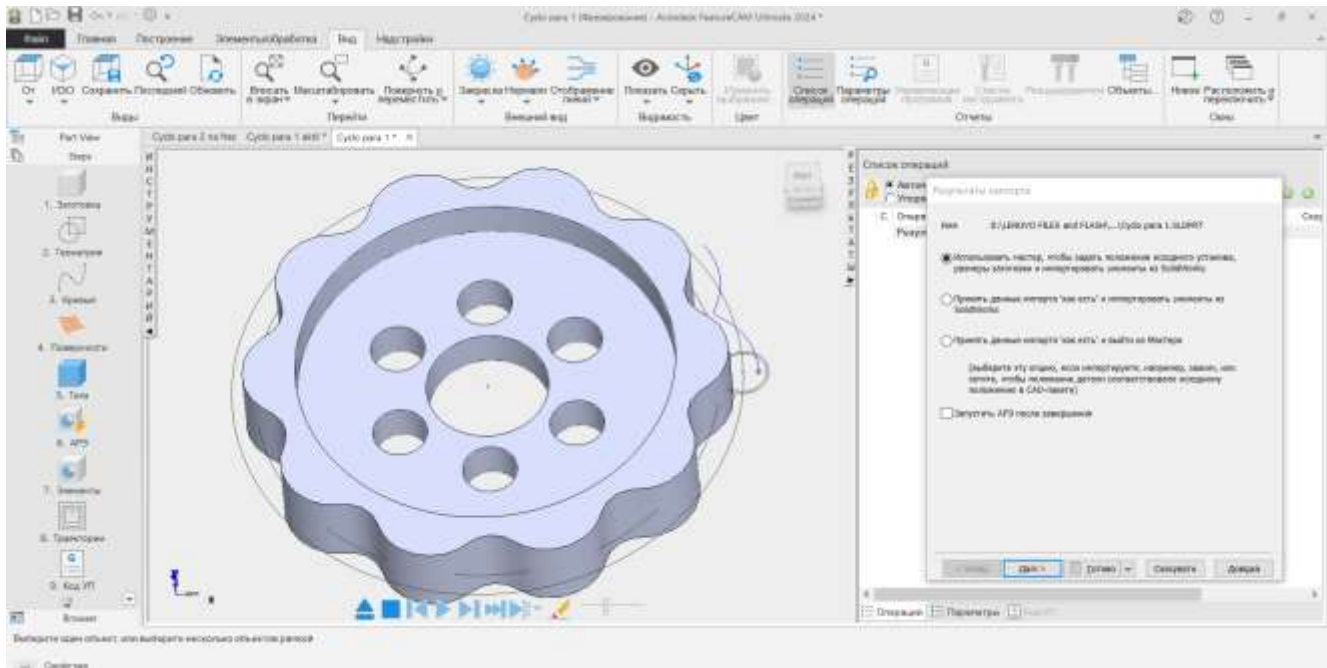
Початок налагодження обробки рухомого колеса
